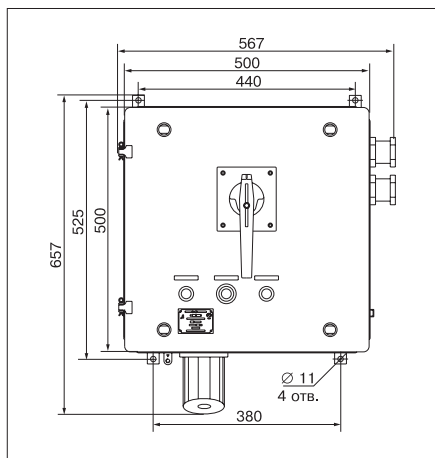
Габаритные и установочные размеры ящика ввода на токи до 63 А однофидерного с одной розеткой.
